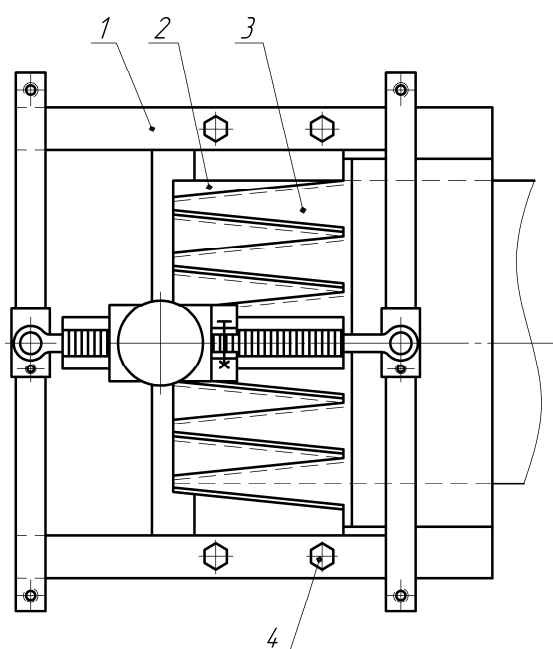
Устройство для разделки концов резиноканевых лент под зубчатый стык
